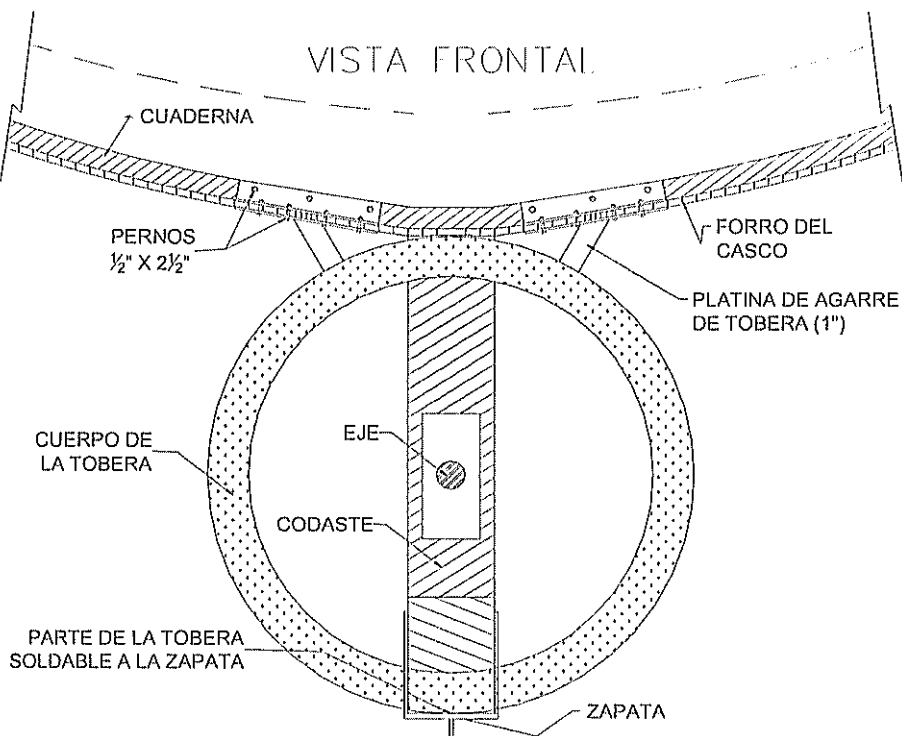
Vista Frontal del Agarre de la Tobera al casco del buque.
